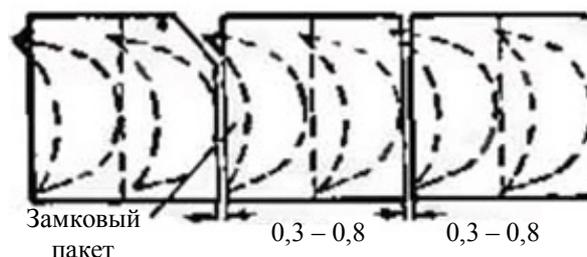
Вид сверху на бандажии сварных пакетов рабочих лопаток с замковым пакетом
